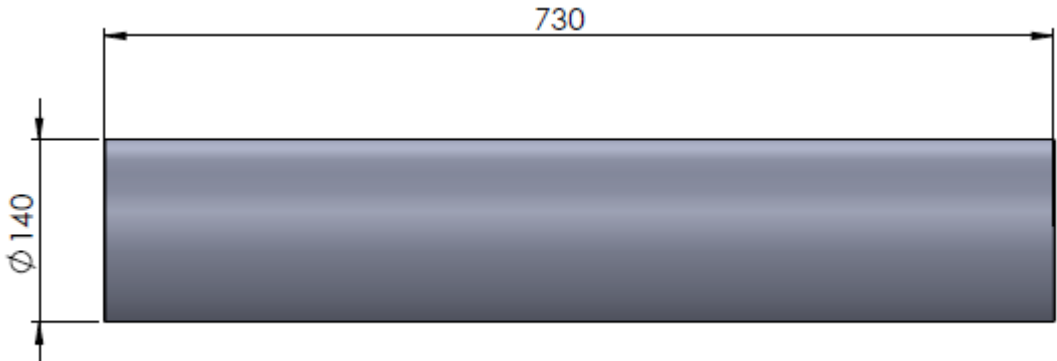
Dessin d'arbre de tambour par SolidWorks
